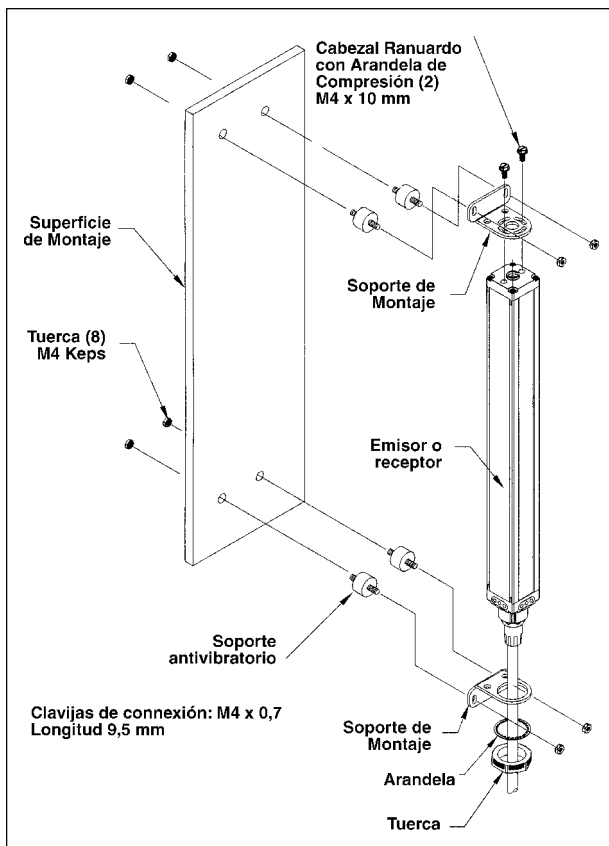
Herramientas de Montaje de Emisor y Receptor
